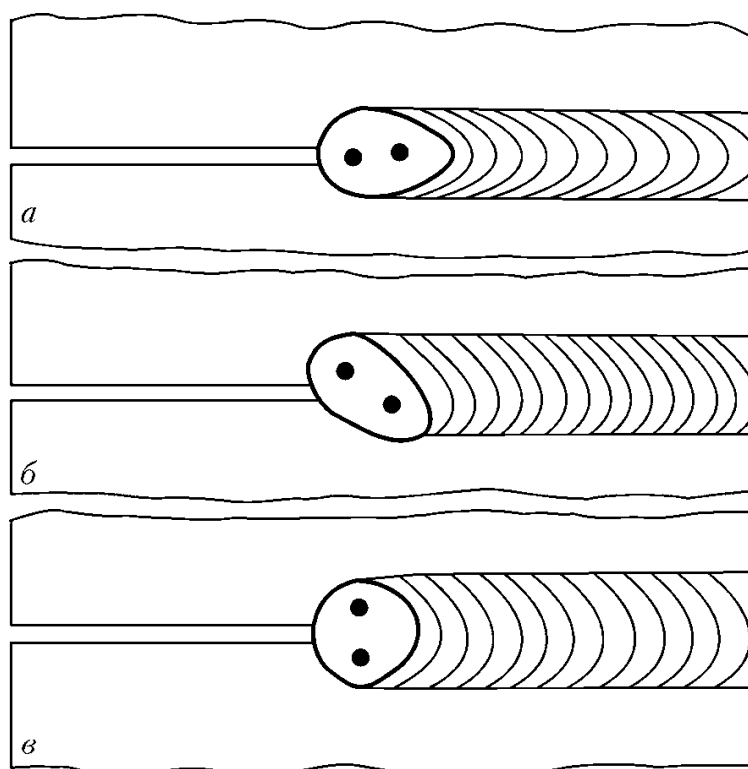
Схема расположения электродных проволок при двухдуговой сварке: а) продольное; б) под углом 45°; в) поперечное
